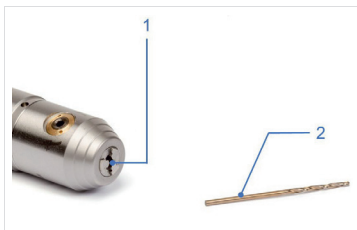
Präzisionsbohrfutter und Werkzeug reinigen
